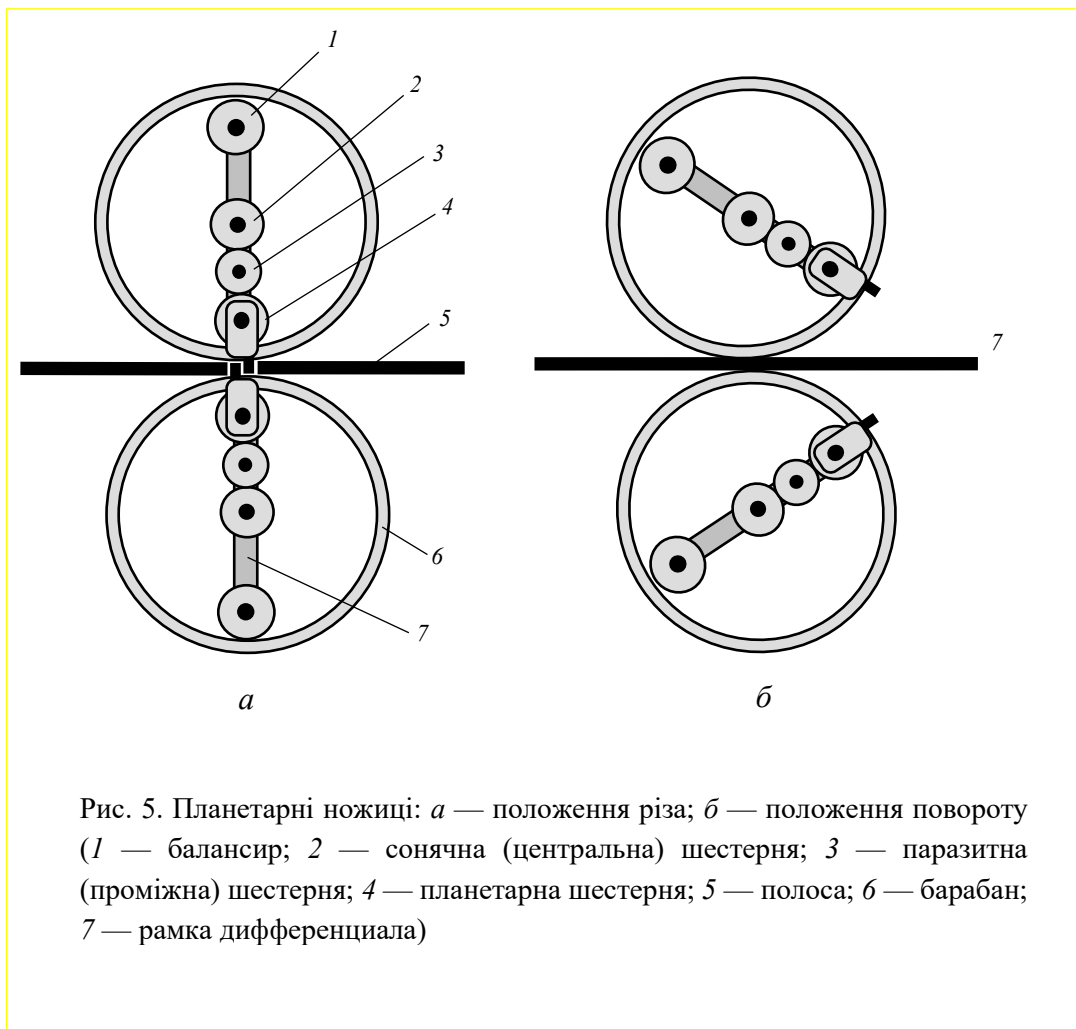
Планетарні ножиці: *а* — положення різання; *б* — положення повороту (1 — балансир; 2 — сонячна (центрально) шестерня; 3 — паразитна (проміжна) шестерня; 4 — планетарна шестерня; 5 — полоса; 6 — барабан; 7 — рамка дифференциала)
